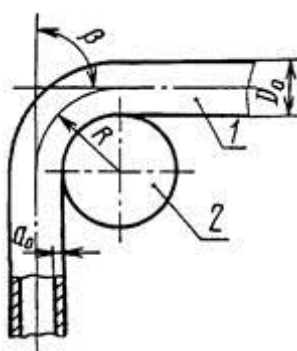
Схема испытания труб на загиб: 1 - образец-патрубок; 2 - цилиндрическая оправка; R - радиус загиба трубы на средней линии; D_0 - наружный диаметр трубы; a_0 - толщина стенки трубы; β - угол загиба
